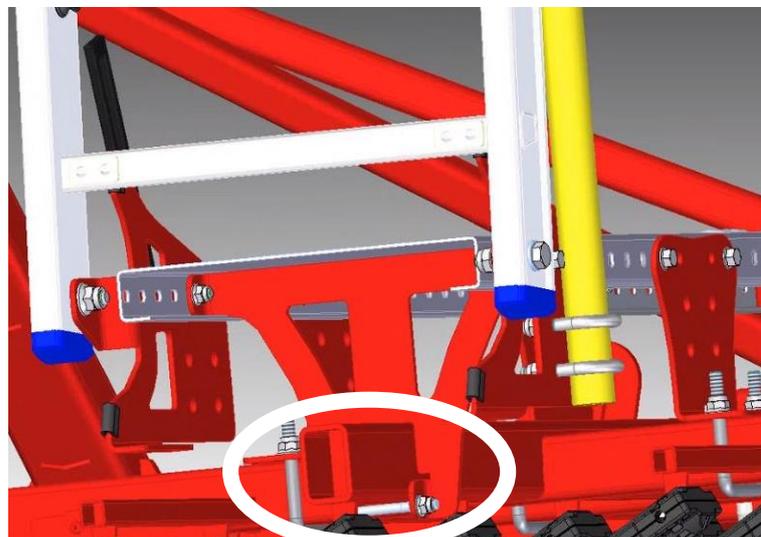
fixation de la plateforme sur le profilé creux à l'aide d'une vis
